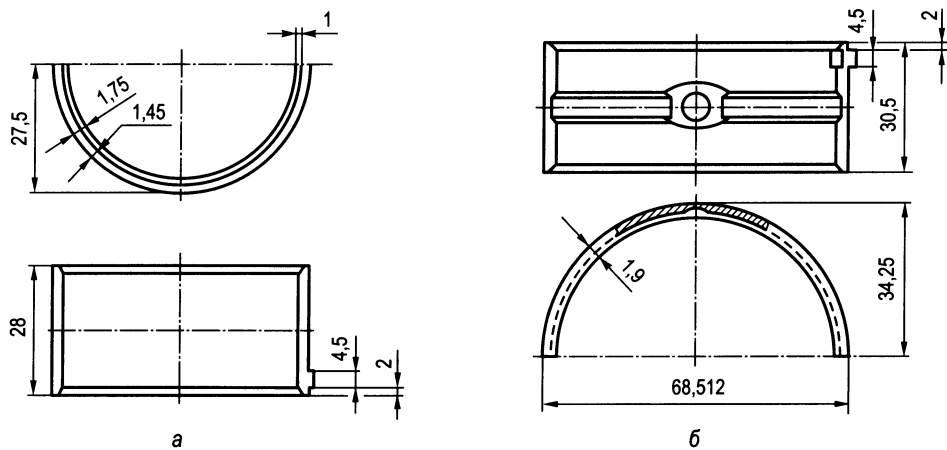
Нижний (а) и верхний (б) вкладыши подшипника
